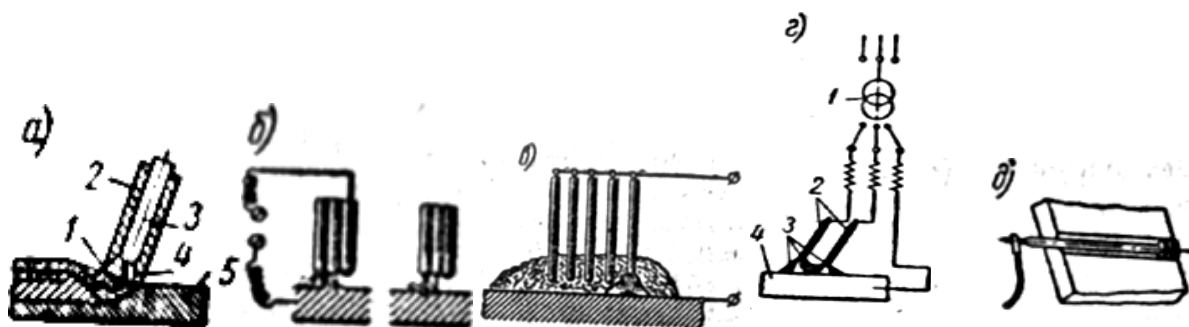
Скоростные методы ручной сварки
